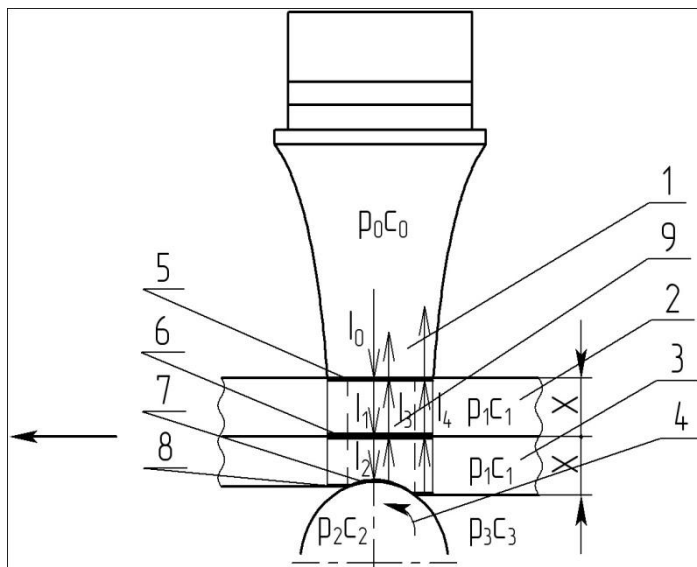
Схема процесса непрерывной шовной УЗ сварки термопластов:
